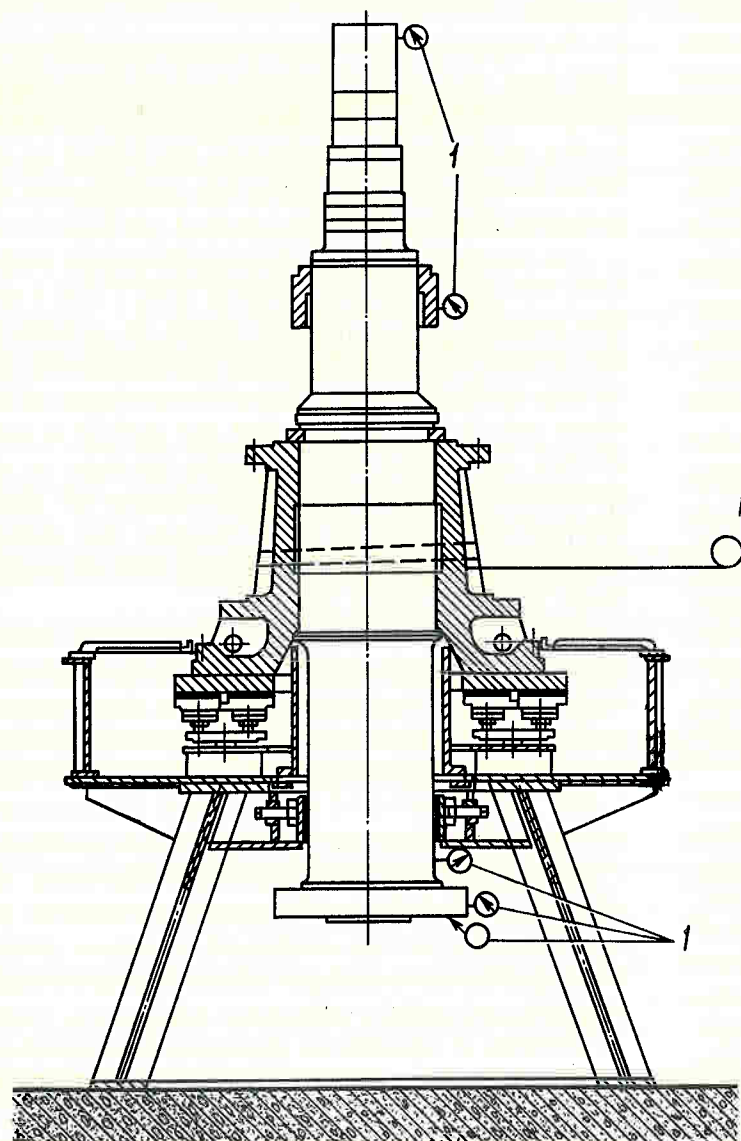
Приспособление для шабрения сегментов подпятника и выверки биения диска на сборочной площадке:
